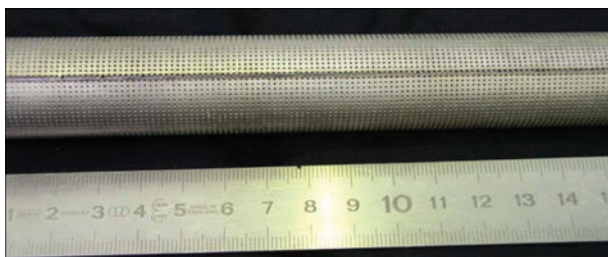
Корпус тонкостенного трубчатого фильтрующего элемента, изготовленного по разработанной технологии лазерной сварки с порошковой присадкой
